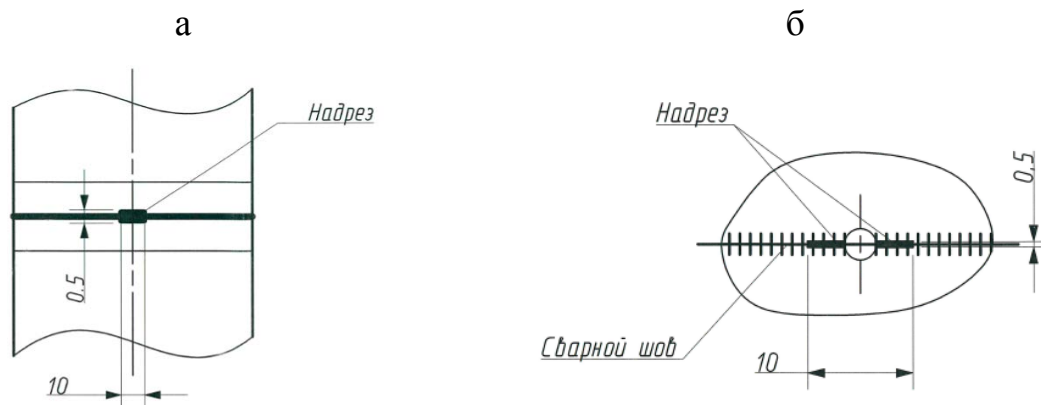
Схема расположения концентраторов напряжений на КПО
